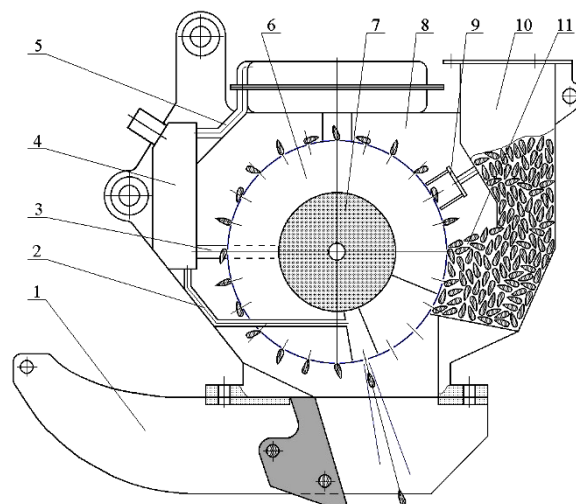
Конструктивно-компоновочная схема предлагаемого высевального аппарата для точного пунктирного посева семян: 1 – сошник; 2 – реверсный канал; 3 – канал разрежения; 4 – блок управления; 5 – канал избыточного давления; 6 – барабан; 7 – шаговый привод; 8 – корпус; 9 – сбрасыватель; 10 – загрузочный канал; 11 – семенная камера
